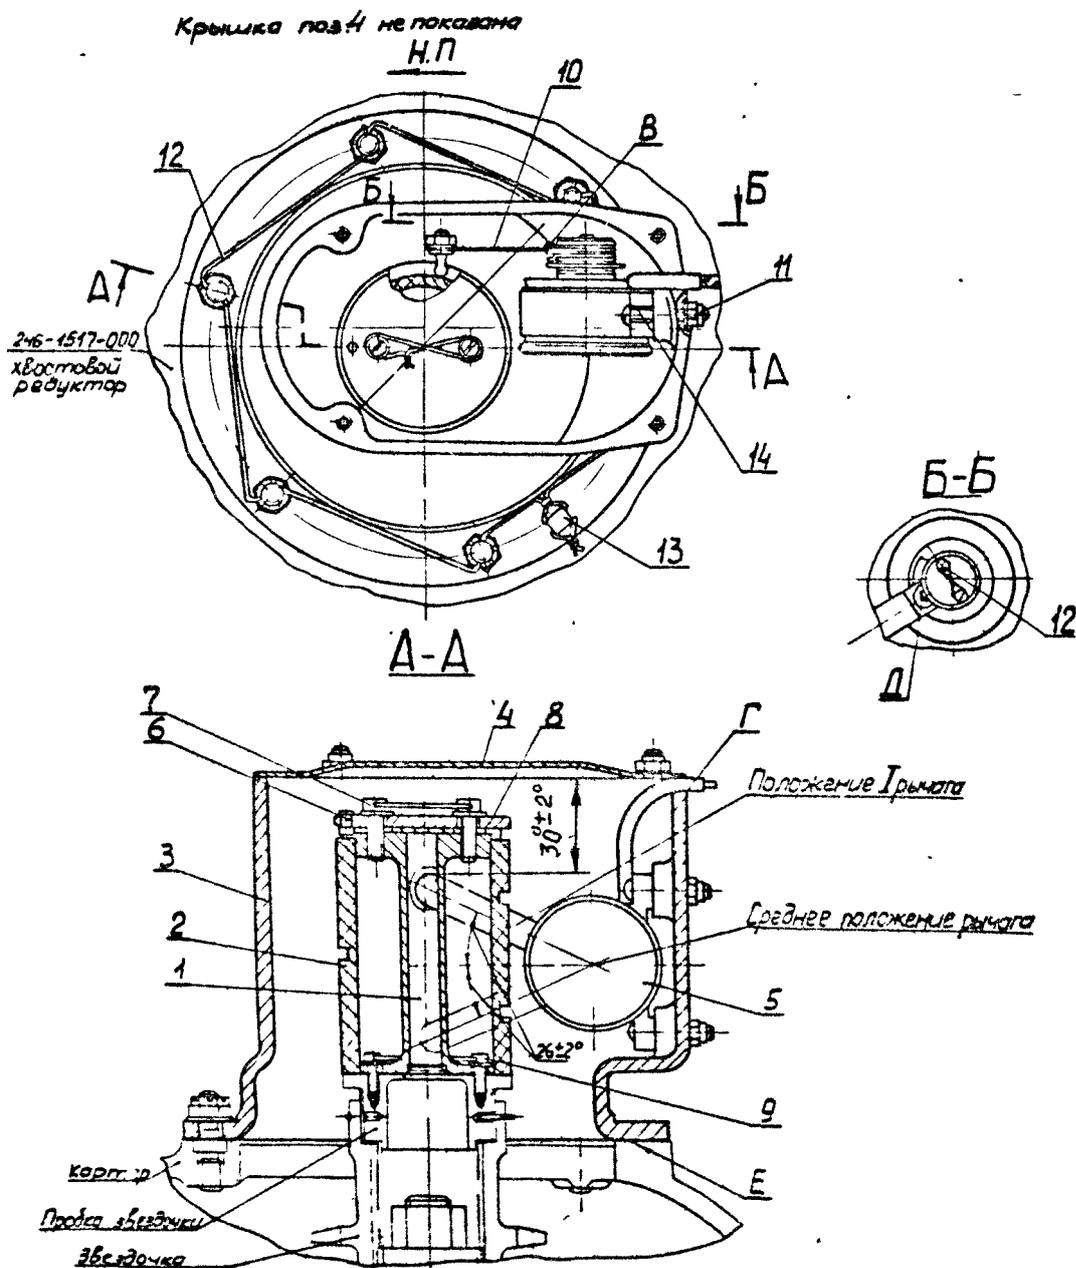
Установка датчика МУ-615А для замера шага рулевого винта
